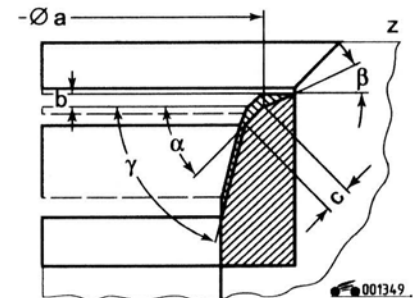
Профиль седла впускного клапана: Z – привалочная поверхность головки блока цилиндров; a = 38,3 мм; c = 1,4–2,0 мм; a = 45°; b = 30°; g = 75°
